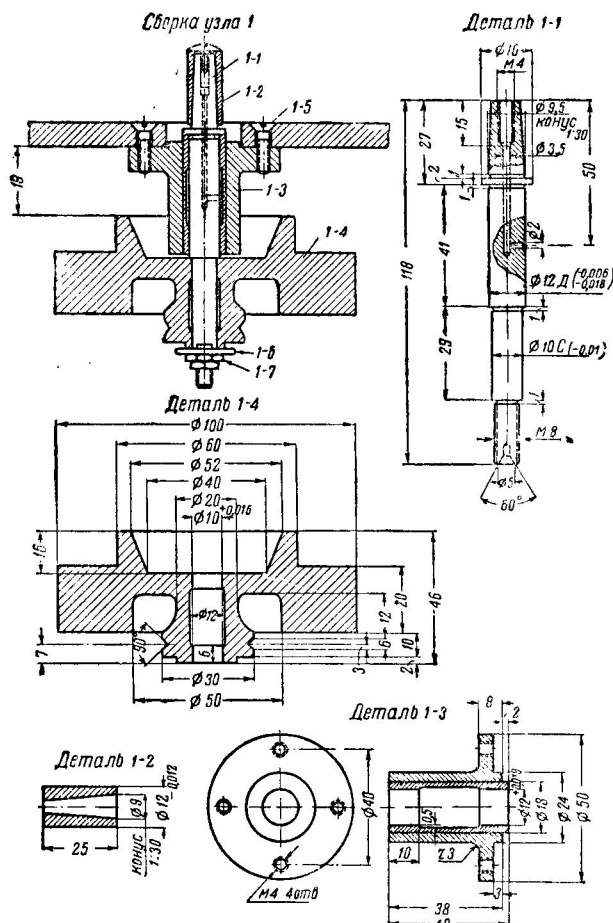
Ведущий ролик (тонвал) с маховиком (узел 1) и его детали: 1-1 — ось (сталь У8А) — 1 шт.; 1-2 — насадка (сталь У8А) — 1 шт.; 1-3 — подшипник (сталь 3) с запрессовкой бронзового вкладыша (БРОЦС6-4-3) — 1 шт.; 1-4 — маховик (сталь С4-21-40) — 1 шт.; 1-5 — винт М4×15 мм (сталь 3) — 4 шт.; 1-6 — шайба 8,5 мм (сталь 3) — 1 шт.; 1-7 — гайка М-8 (сталь 3) — 2 шт.
